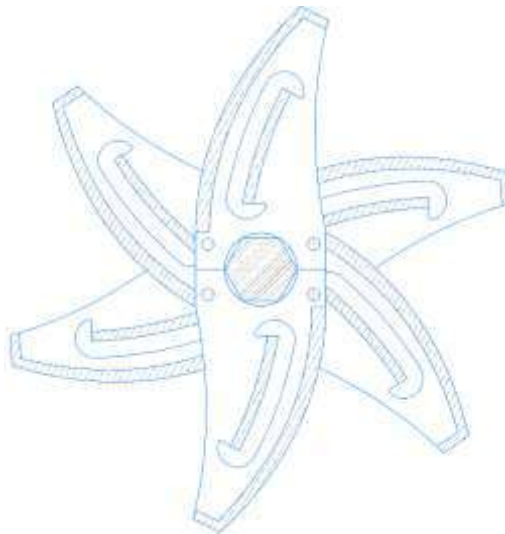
Ножевая головка с модифицированными куттерными ножами
